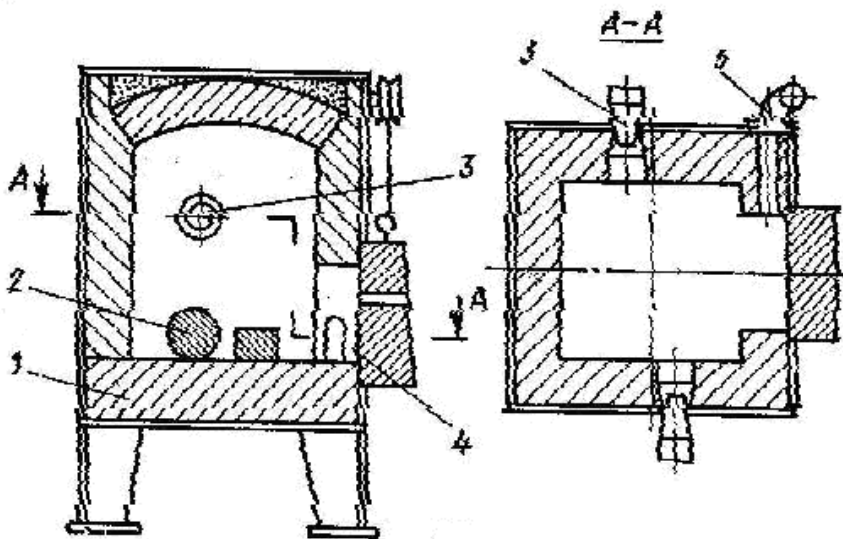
Камерная нагревательная печь: 1 – под печи, 2 – заготовки, 3 – форсунки, горелки, 4 – окно загрузки-выгрузки заготовок, 5 – дымоход
